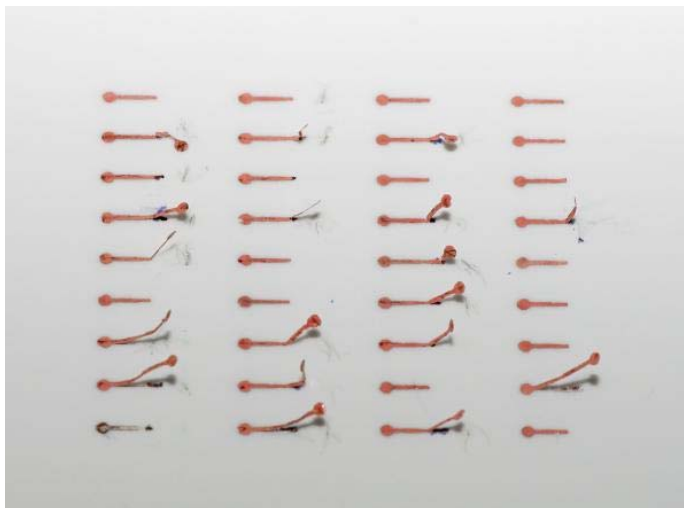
Detail částečně odtržené pružné měděné plošky
